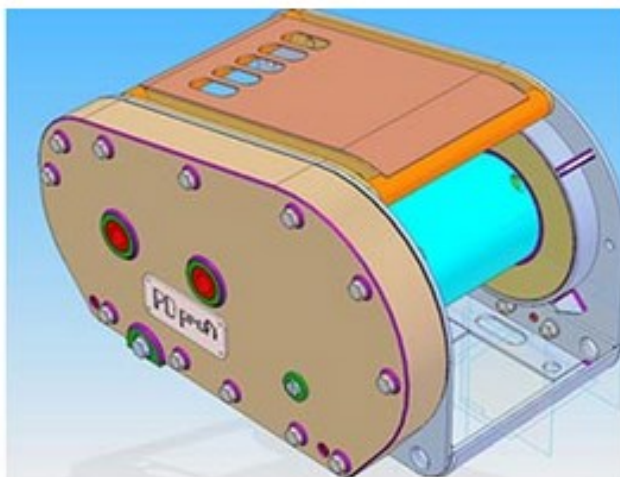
Pneumatické manipulační zařízení ZMPP 1,6t/3,2t [9]
